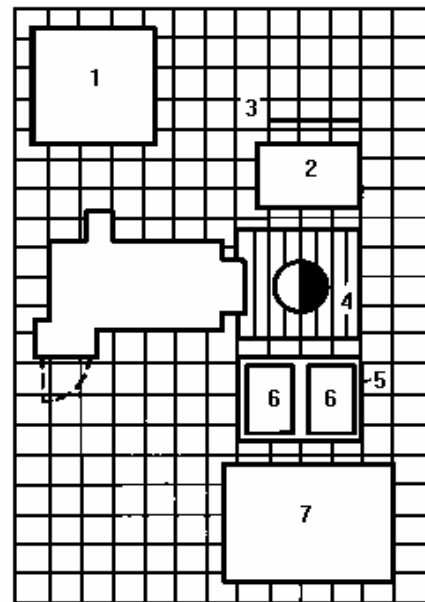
Безпечна організація робочого місця свердлильника, що обслуговує вертикально-свердлильний верстат (1 - стелаж; 2 - інструментальна тумбочка; 3 - планшет; 4 - штахет; 5 - приймальний стіл; 6 - тара; 7 - стелаж-підставка)
